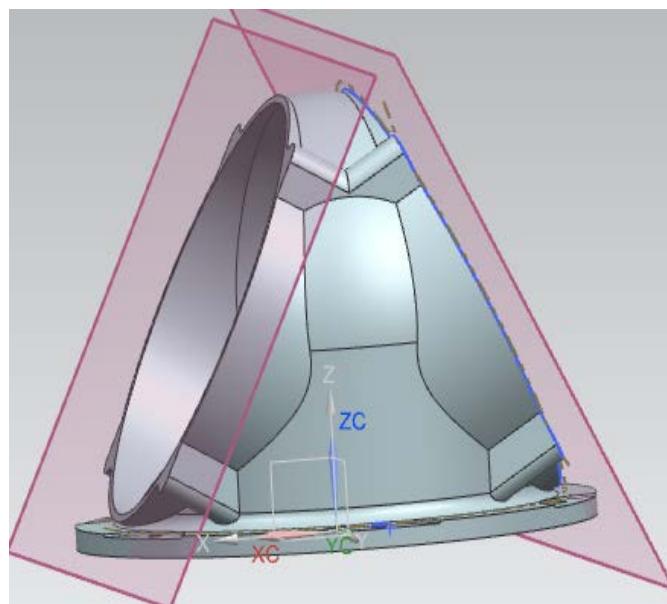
3D модель корпуса с фланцевыми частями
